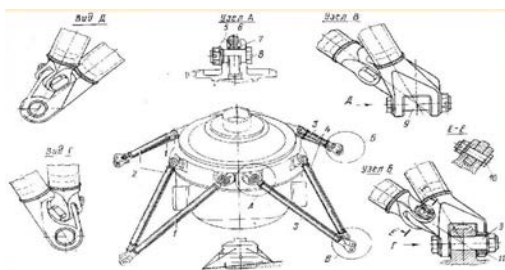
Схема кріплення редуктора вертольота Ми-8.
